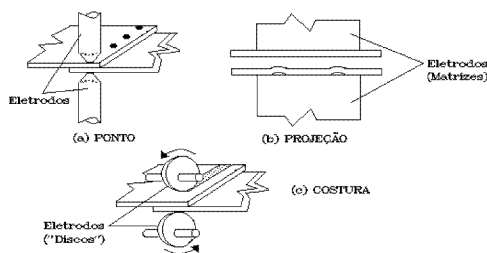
Principais Métodos de Soldagem por Resistência Elétrica.
